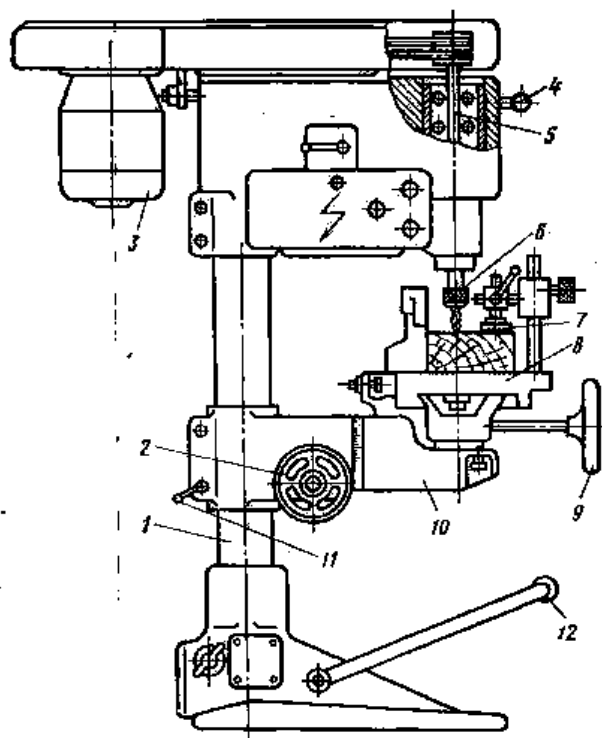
Сверлильно-пазовальный вертикальный станок с ручной подачей СВП-2:
